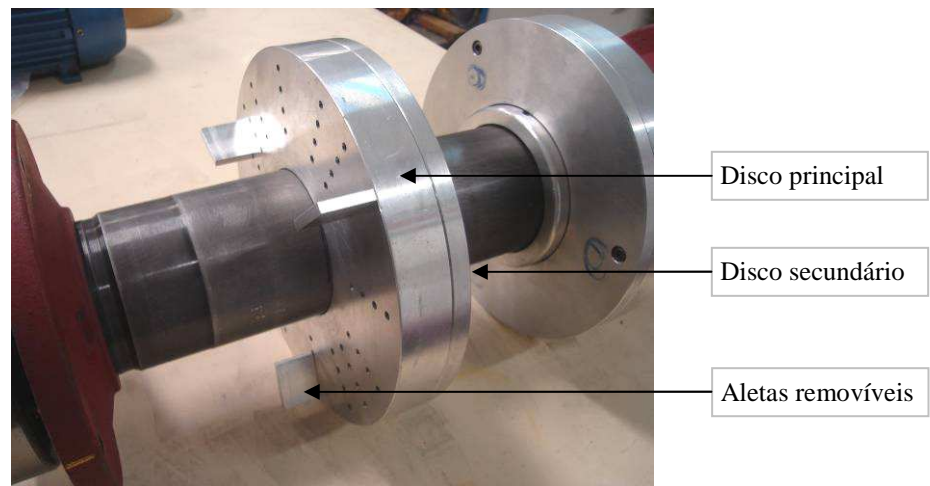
Rotor cambiável, com sistema intercambiável de aletas.
